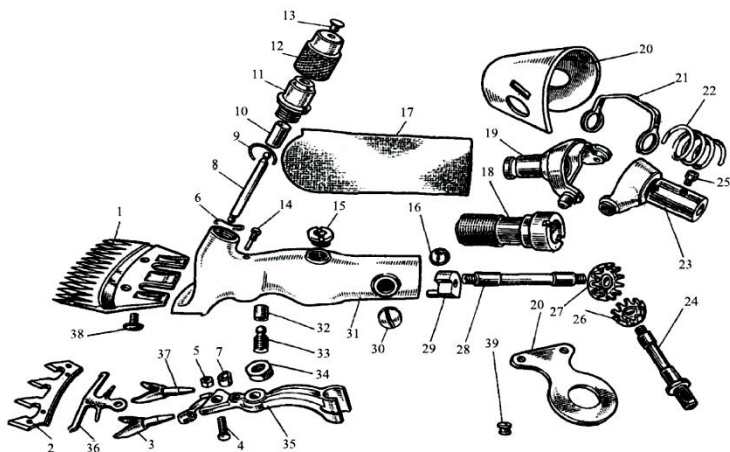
Узлы и детали стригальной машинки МСО-77Б: 1 - гребёнка; 2 - нож; 3 - левая нажимная лапка; 4 - винт крепления фиксирующей пружины; 5 - гайки; 6 - пружина-державка упорного (нажимного) стержня; 7 - подпятник упорного (нажимного) стержня; 8 - упорный (нажимной) стержень; 9 - стопорное пружинное кольцо; 10 - нажимной патрон; 11 - штуцер нажимного механизма; 12 - нажимная гайка; 13 - упор нажимного патрона; 14 - предохранительный винт рычага; 15 - заглушка смотрового окна; 16 - сферический ролик; 17 - чехол корпуса машинки; 18 - втулка корпуса; 19 - внутренний защитный кожух; 20 - рубашка защитного кожуха; 21 - замок шарнира; 22 - пружина; 23 - наружный защитный кожух; 24 - передаточный валик; 25 - стопор; 26 - малое ведущее зубчатое колесо (шестерня $Z1 = 10$); 27 - большое ведомое зубчатое колесо (колесо $Z2 = 12$); 28 - валик эксцентрика (эксцентриковый валик); 29 - эксцентрик с пальцем; 30 - заглушка смазочного окна; 31 - корпус машинки; 32 - подпятник рычага; 33 - центр вращения; 34 - контргайка центра вращения; 35 - рычаг; 36 - фиксирующая пружина; 37 - правая нажимная лапка; 38 - винт крепления гребёнки; 39 - заклёпка
